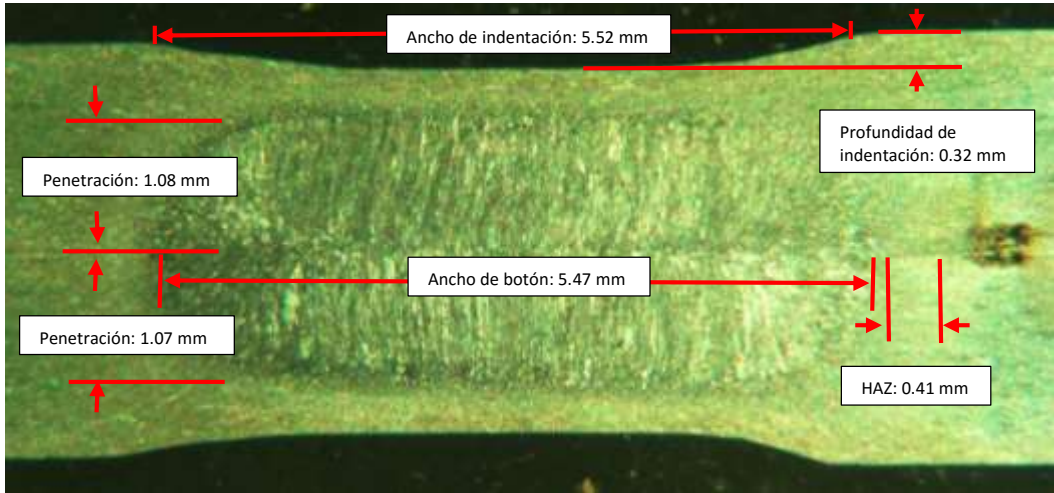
Mediciones realizadas en el botón de soldadura número 14.
